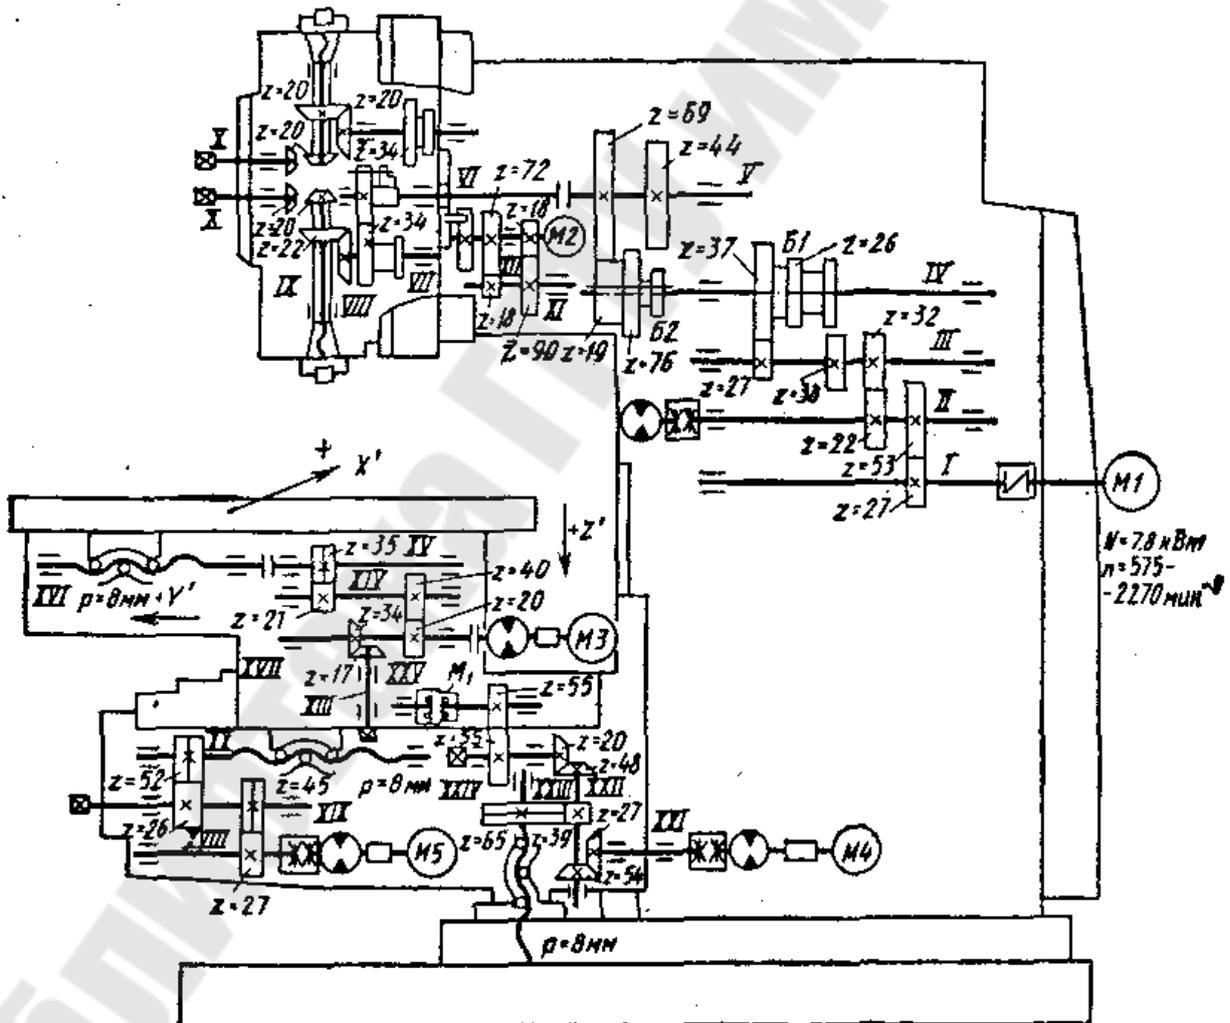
Кинематическая схема вертикально-фрезерного станка с ЧПУ
